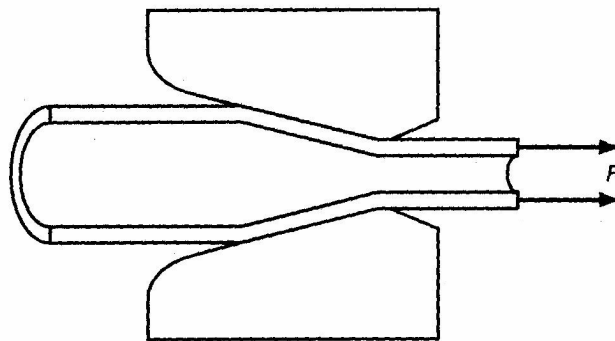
Estirado de tubos sin mandril (entallado de tubos).
